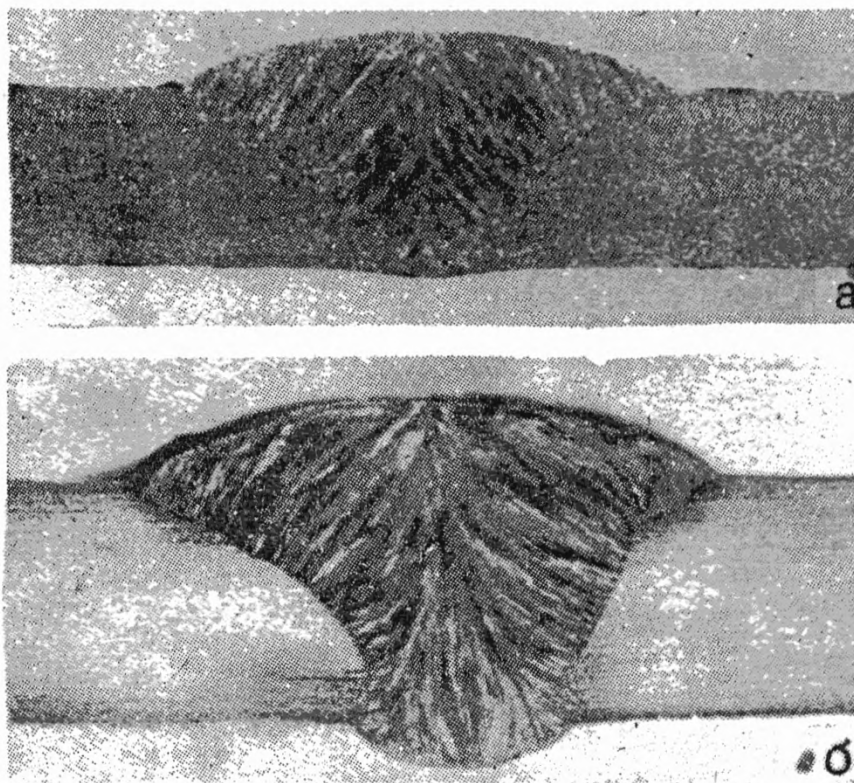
Сварка в один проход стыкового соединения:
